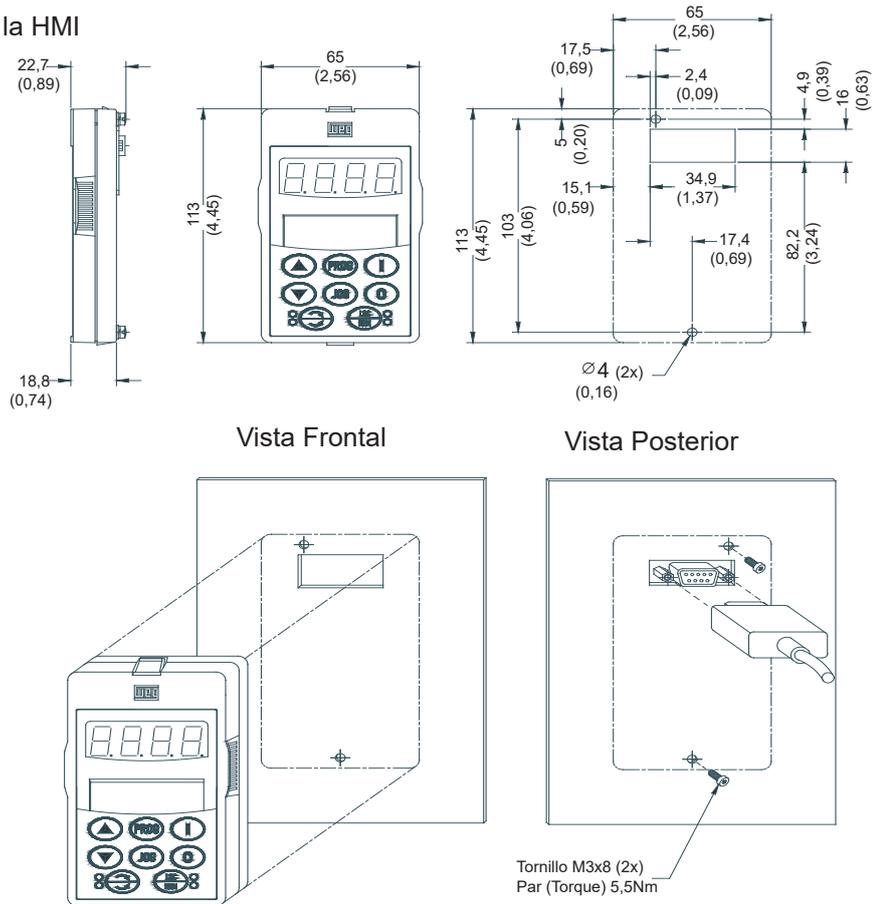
Dimensiones en mm (in) y instalación de la HMI en el panel sen moldura
